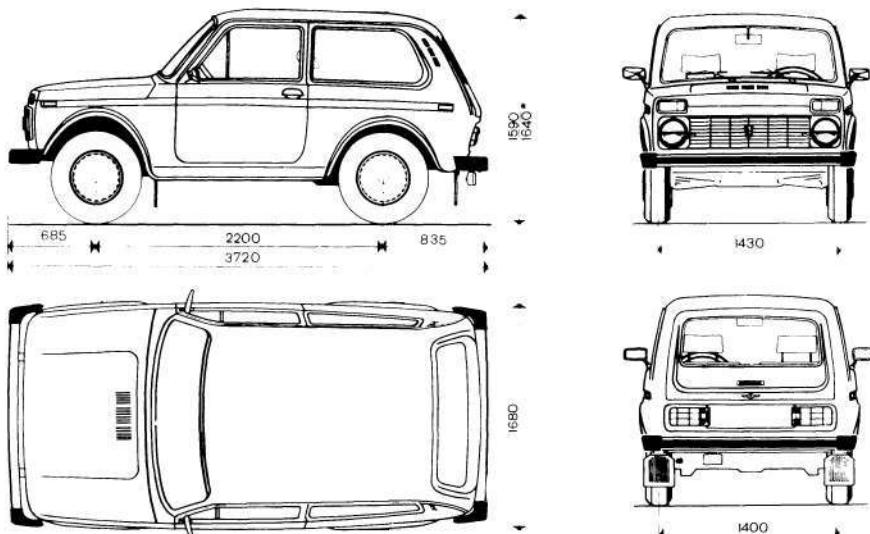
Габаритные размеры (размер со звездочкой — высота без нагрузки)
